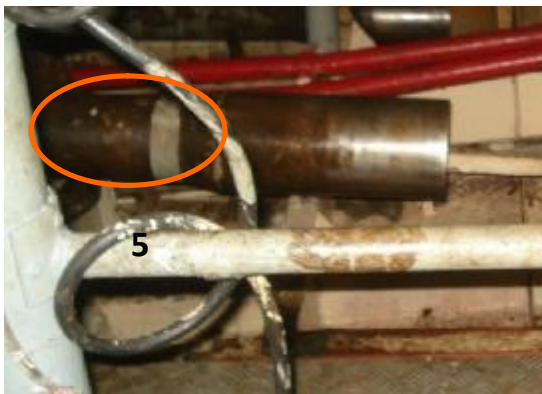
c: Extensómetro 5. Sobre el eje intermedio
